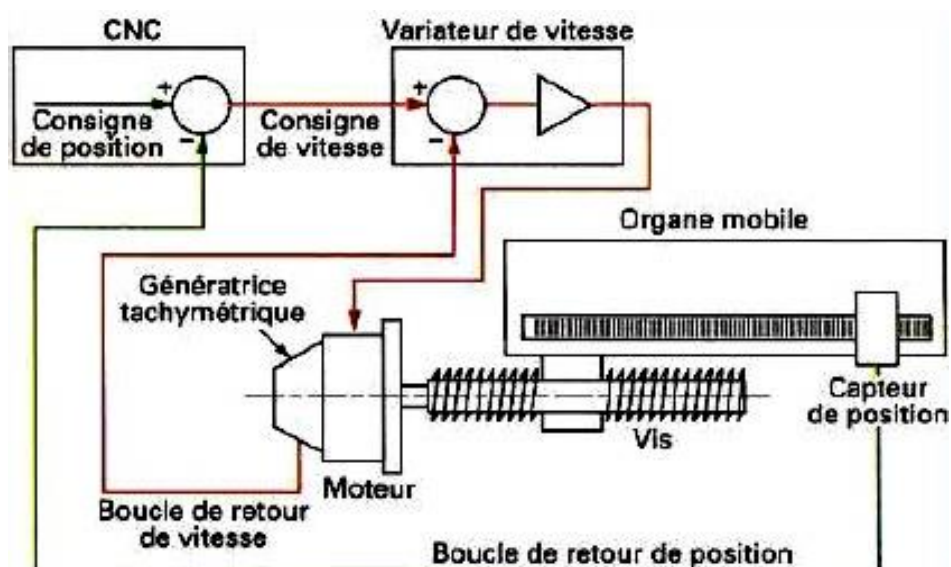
Schéma explicatif pour l'asservissement de la machine.
